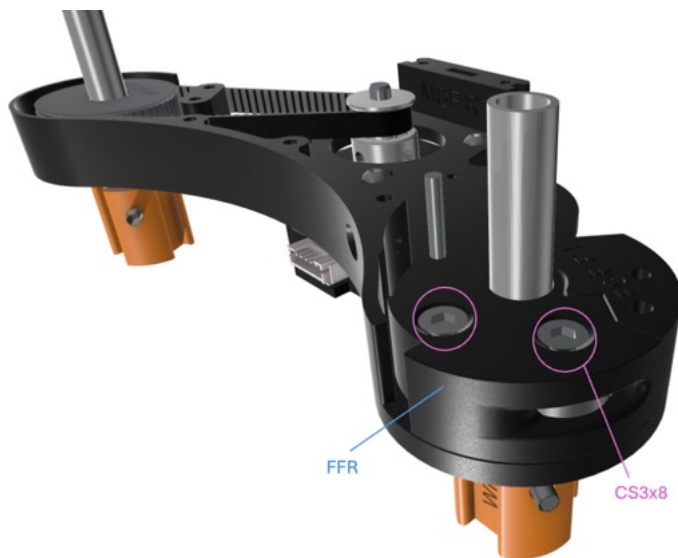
Rewinder-Chassis Montageschritt 13.
